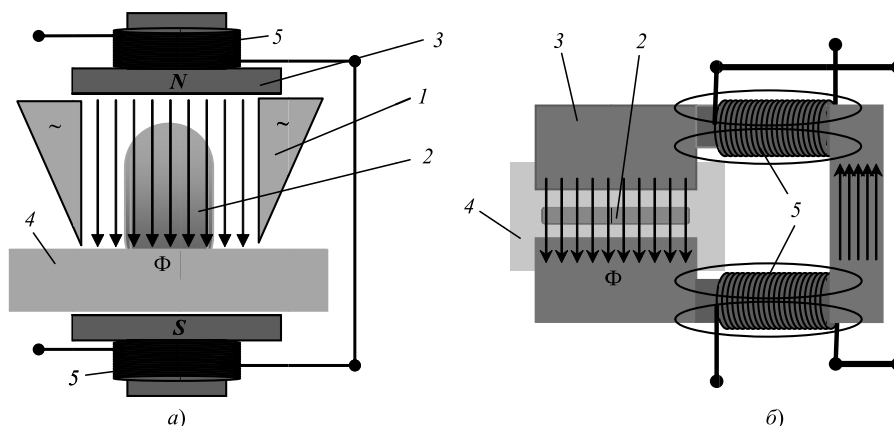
Схемы создания магнитного поля в сварочной ванне:
